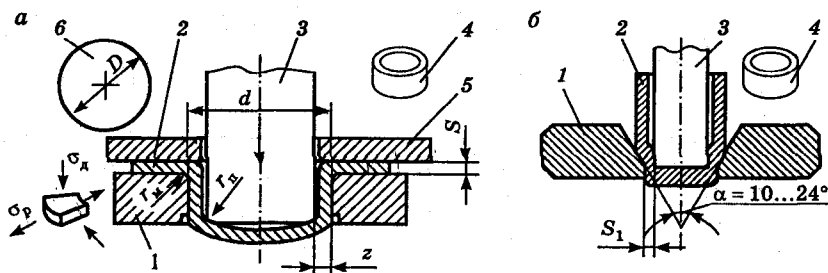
Схемы вытяжки без утонения (а) и с утонением стенки (б): 1 — матрица; 2 — деформируемая заготовка; 3 — пуансон; 4 — изделие; 5 — прижим; 6 — исходная заготовка; r_m , r_n — радиус закругления матрицы и пуансона; α — угол штамповочного уклона матрицы
